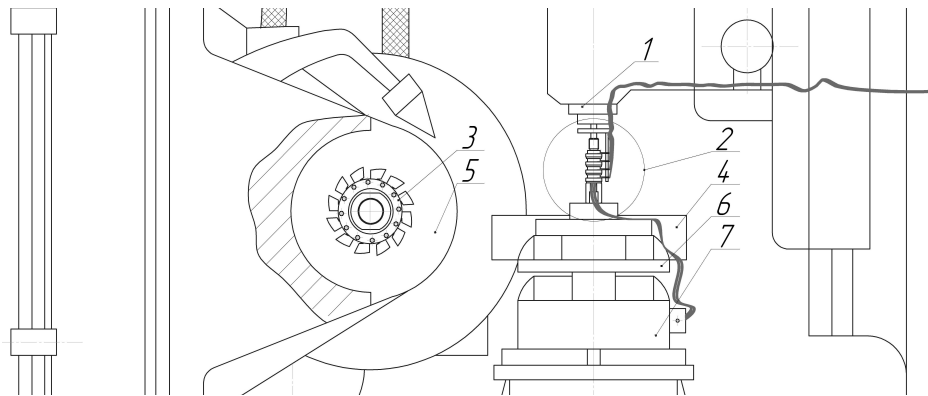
Эскиз приспособления для закрепления образцов, имитирующих одну впадину зубчатого колеса
